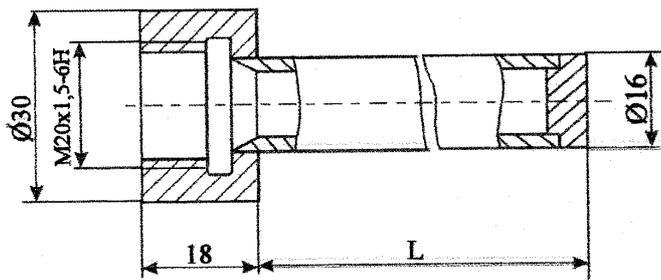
Габаритные и установочные размеры вычислительного блока ИВБ.
